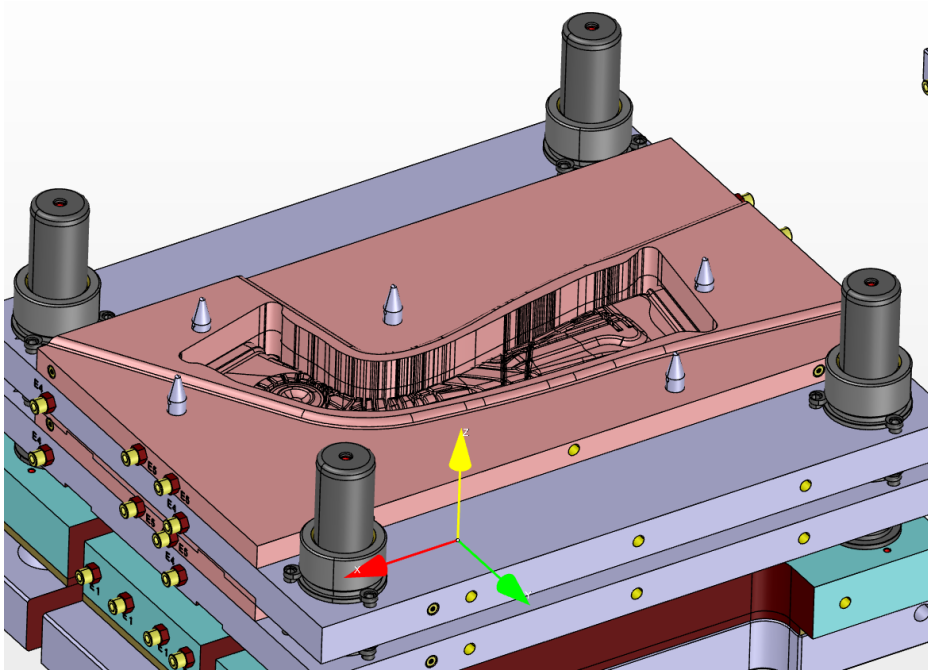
Demonstrator Werkzeug UT [Quelle: Schmidt Modellbau GmbH]
